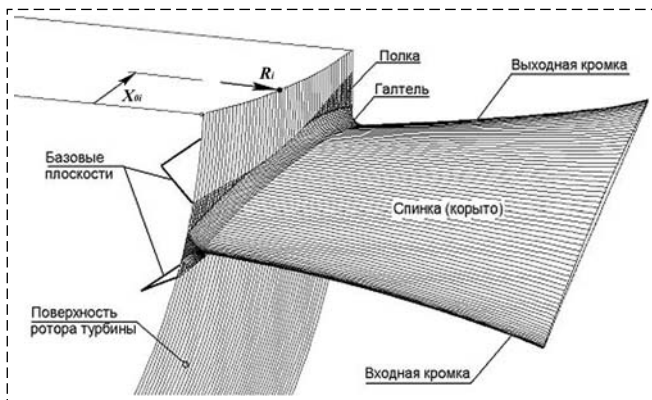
Обрабатываемая поверхность пера лопаток ГТД
